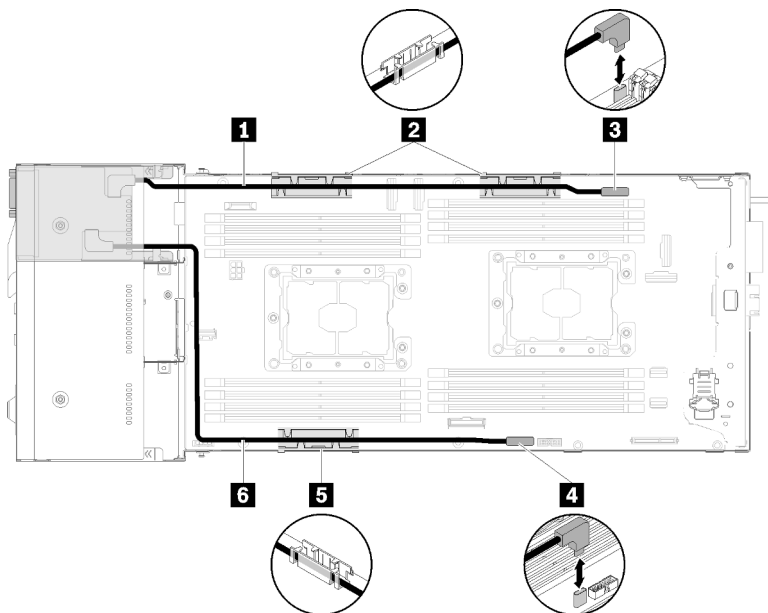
Disposición de los cables del módulo multiconector de KVM izquierdos
